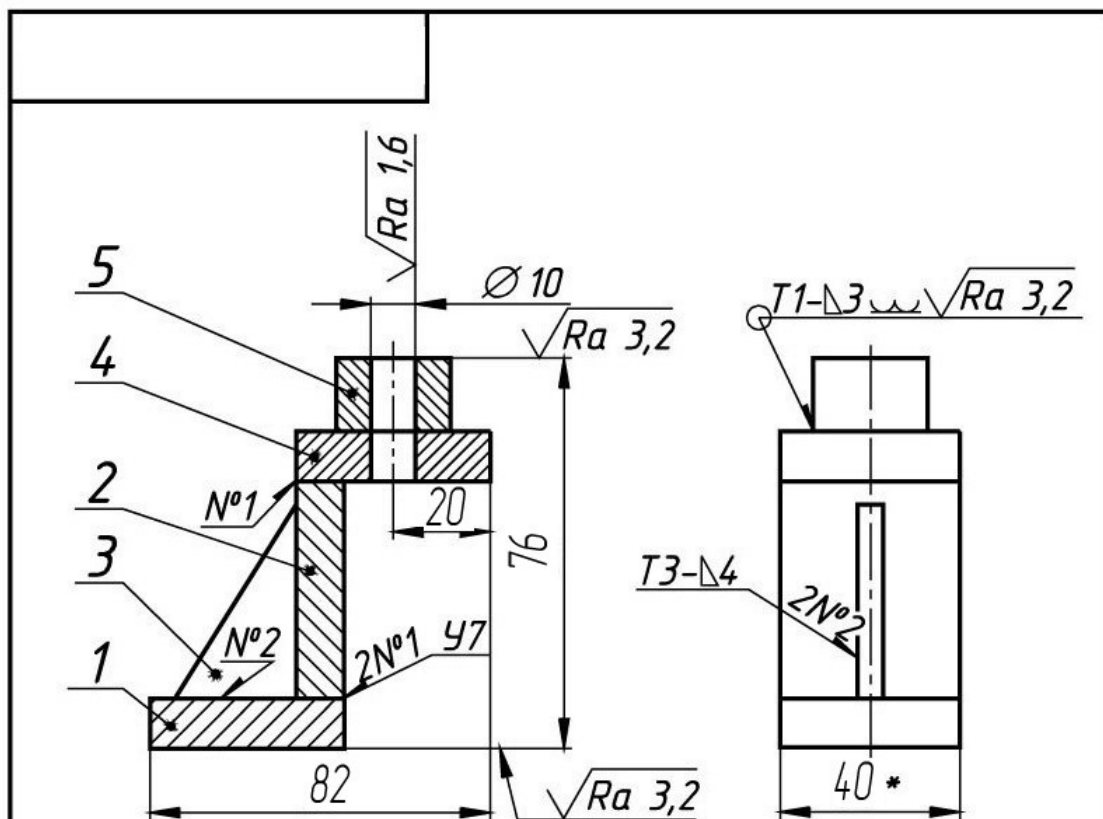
Образец задания для практической работы «Соединение сварное»
